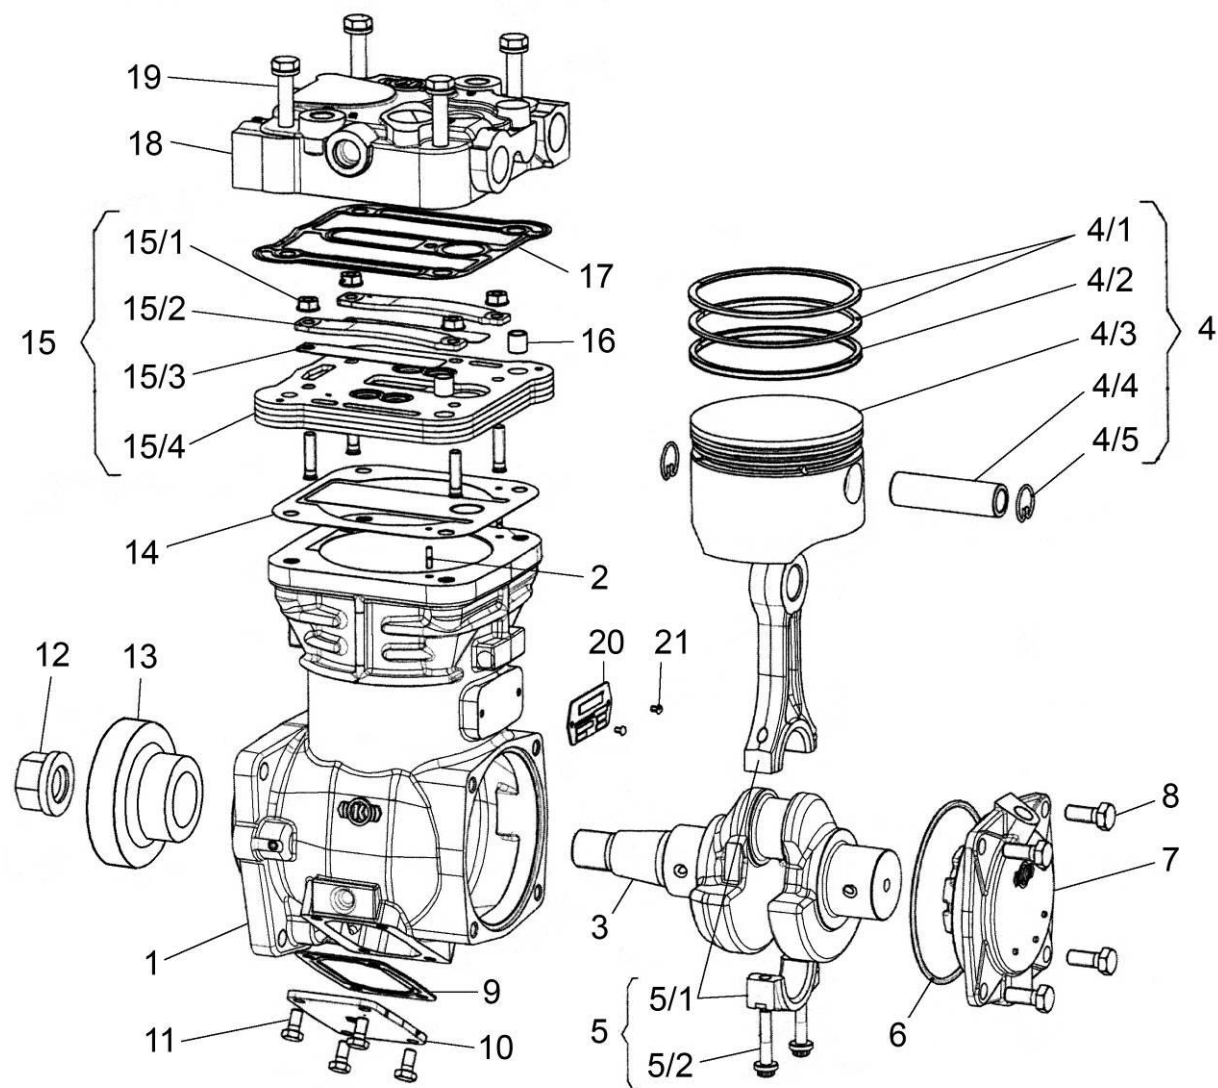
а Компрессор пневматического тормоза LP 3999. Устройство
